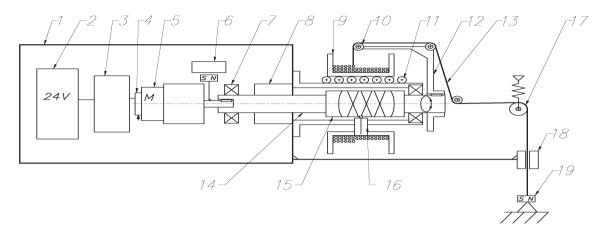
Схема новой встроенной лебедки автономного привязного профилирующего аппарата «Винчи»: 1 — сухой отсек аппаратурного корпуса, 2 — аккумуляторная батарея, 3 — модуль управления, 4 — тормоз, 5 — мотор-редуктор, 6 — датчик оборотов, 7 — подшипник двухрядный, 8 — керамический сальник, 9 — барабан, 10 — укладочный ролик, 11 — шариковые линейные направляющие, 12 — водило, 13 — трос, 14 — выходной вал, 15 — винт с двунаправленной резьбой, 16 — челнок, 17 — датчик натяжения, 18 — датчик конца троса, 19 — концевой магнит
